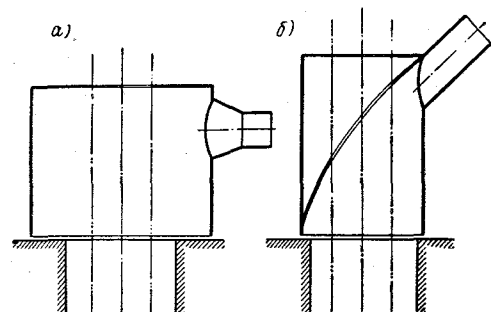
Пылеулавливающий колпак: а — обычной конструкции; б — предлагаемой конструкции.
